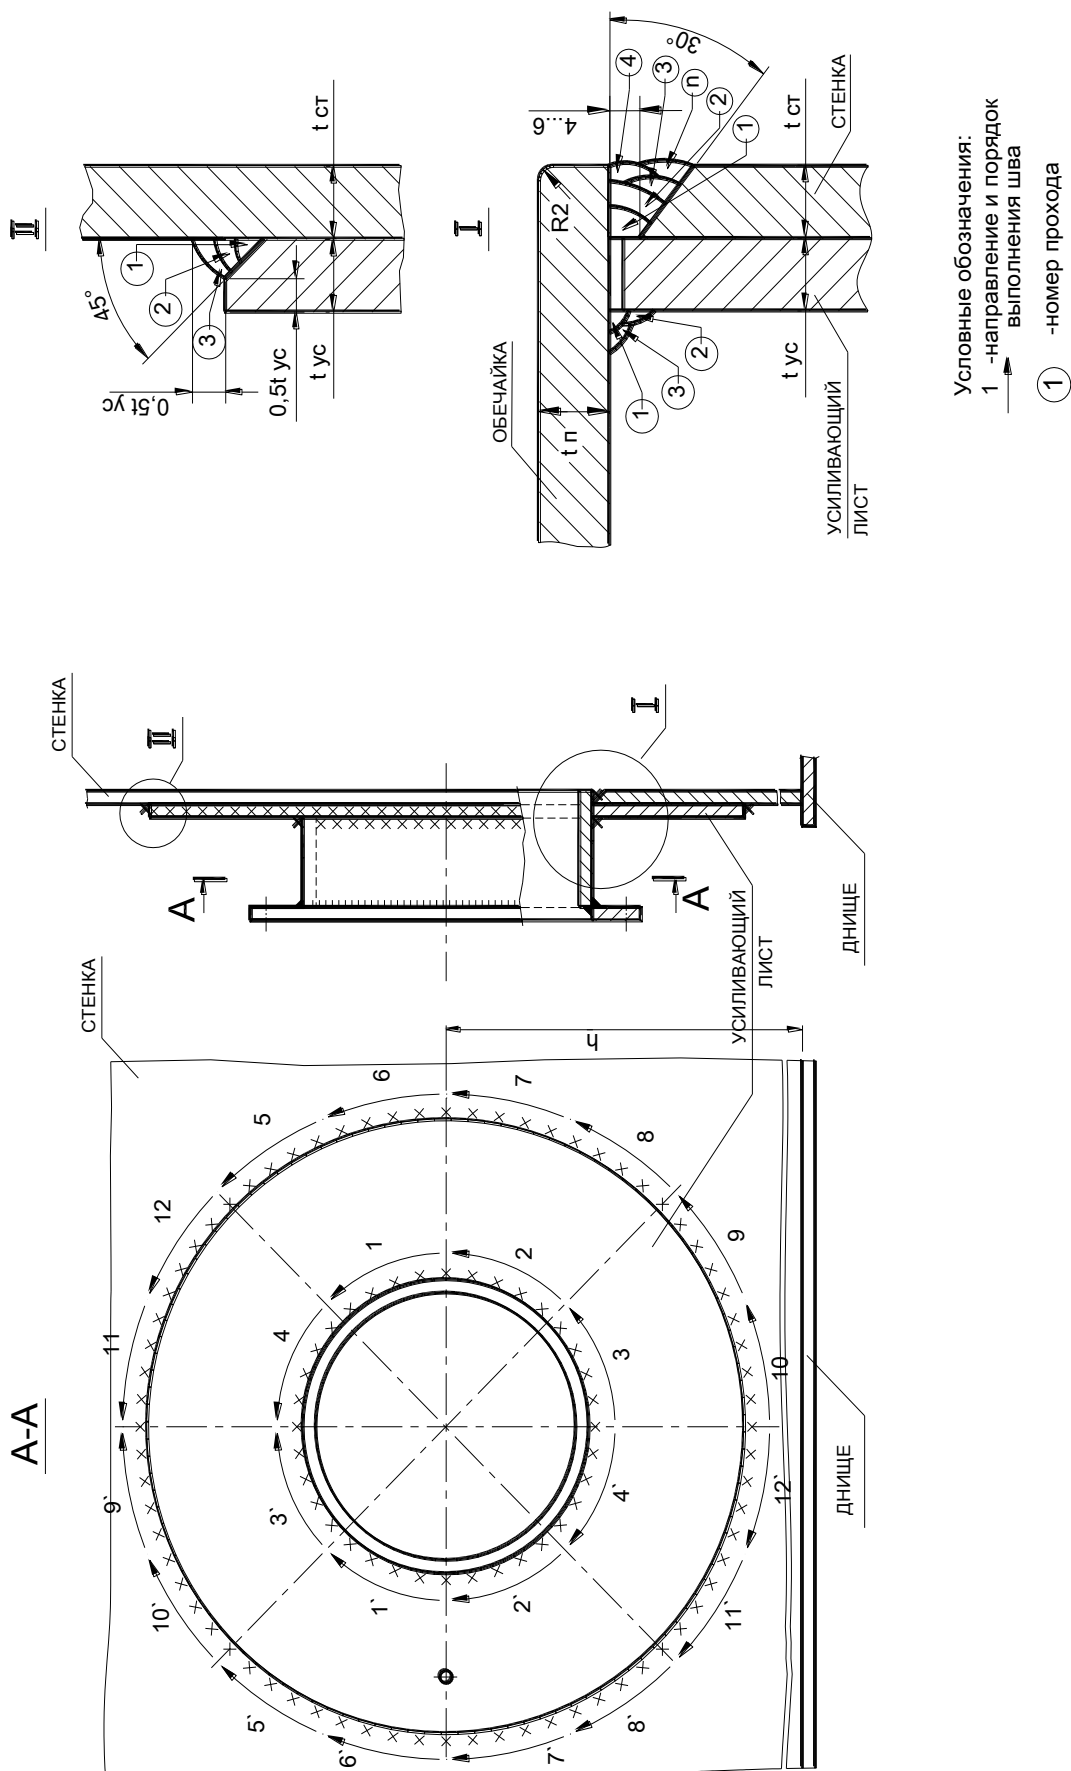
Схема сварки круглого люка-лаза в стенке
